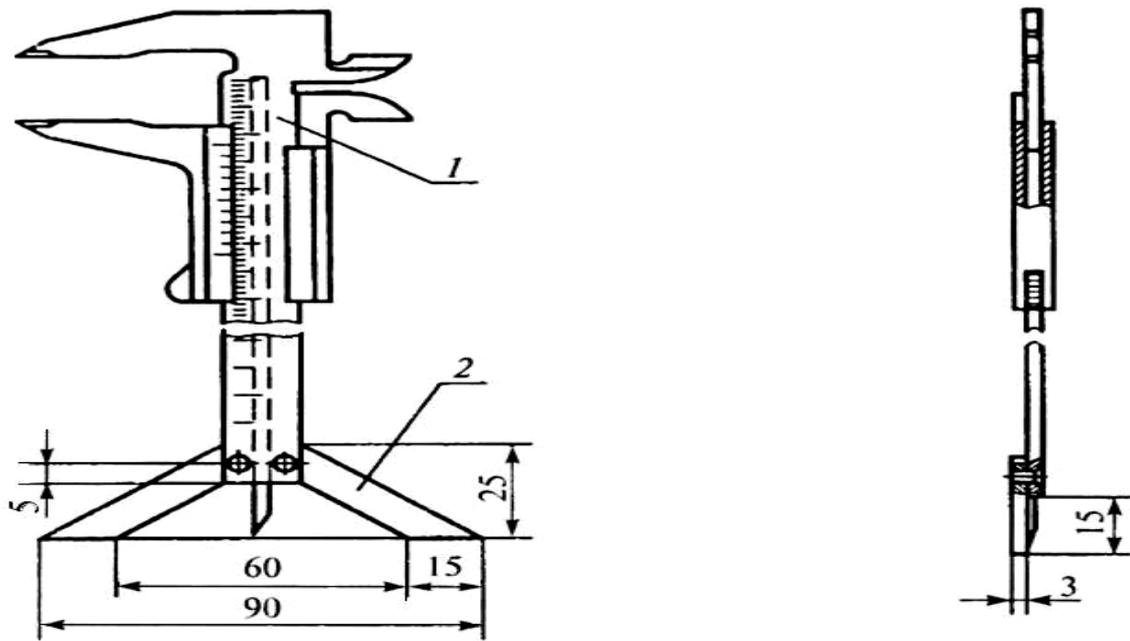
Штангенциркуль типа «ШЦ-1» с опорой: 1 – штангенциркуль; 2 – опора
